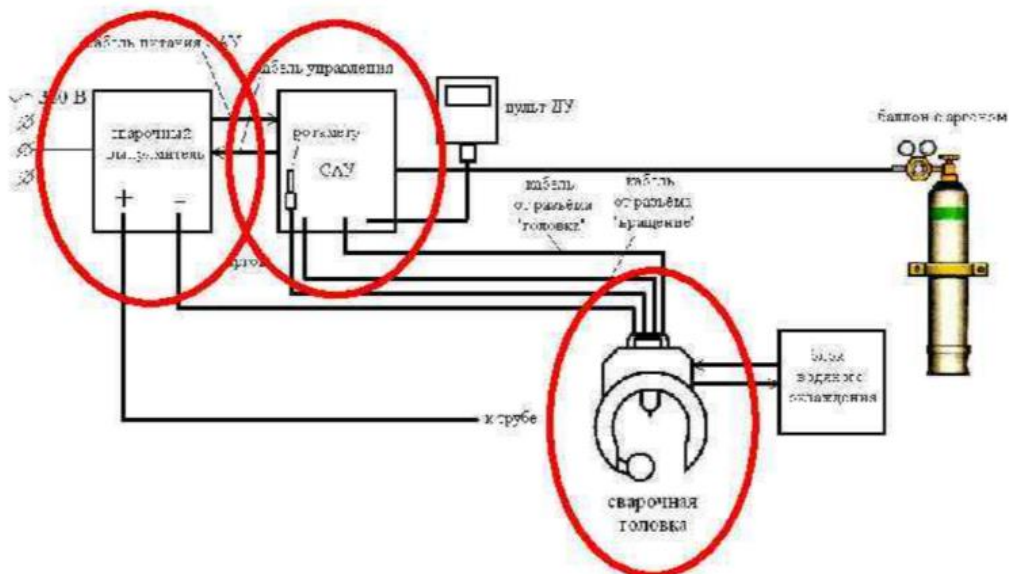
Схема поста автоматичної аргонодугового зварювання неповоротних стиків труб
